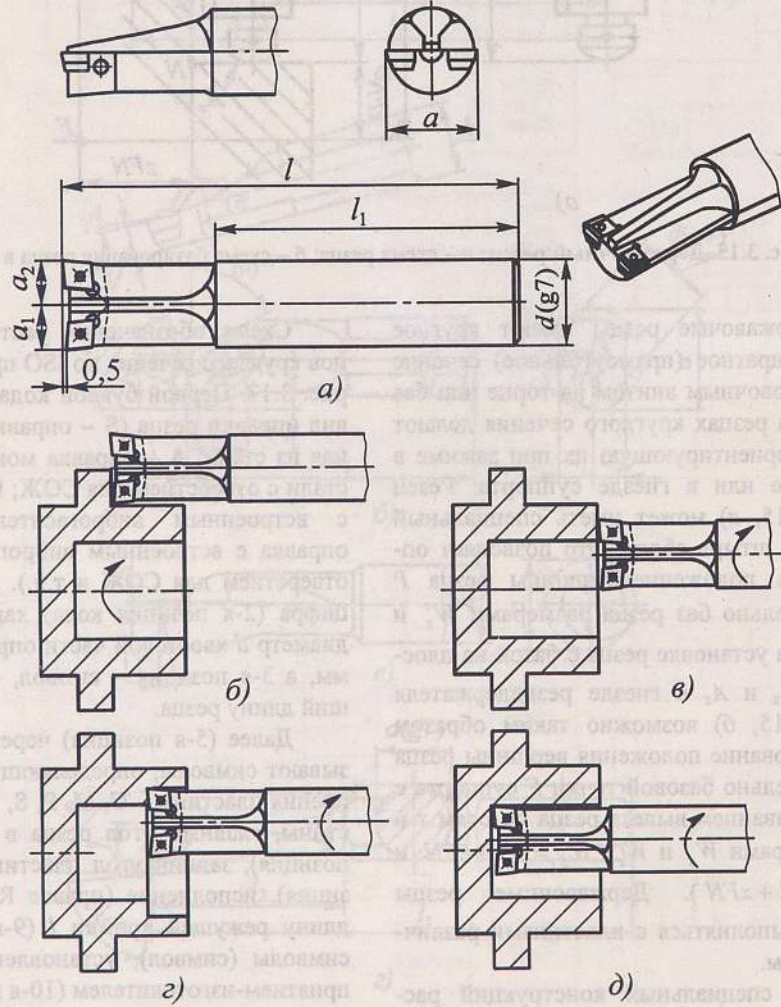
Расточный резец с двумя пластинами и схема его использования:
